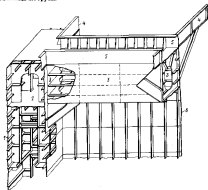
Подпалубный бортовой коридор судна с двойными бортами, соединенный с коридором противолобного борта и палубными коридорами, используемый поперечной переборкой
